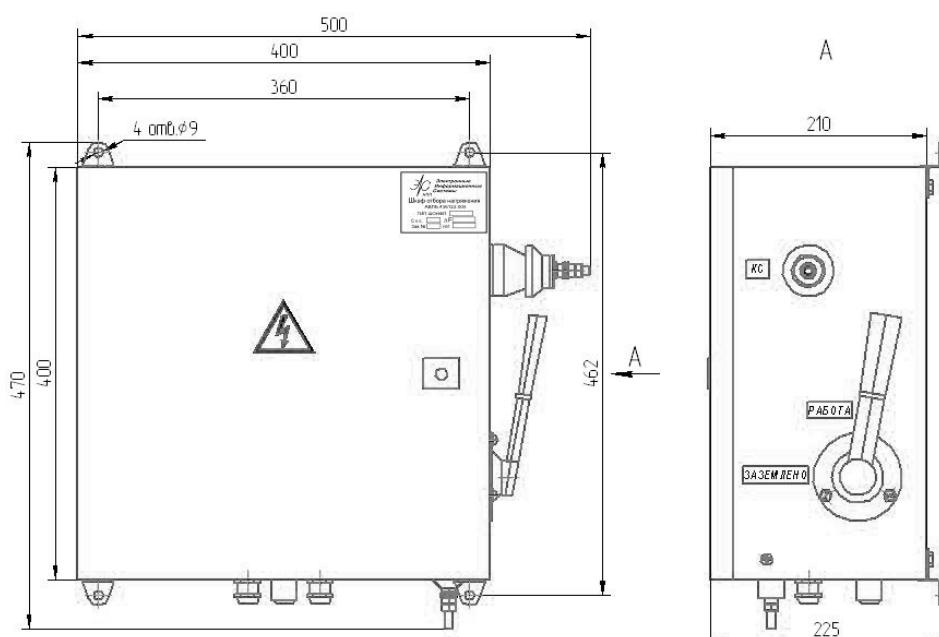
Габаритно-присоединительный чертеж Фильтр-ШОН.
